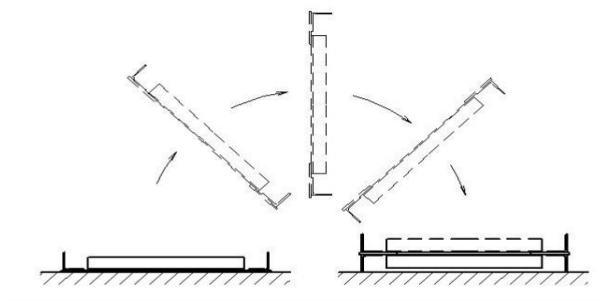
Поворот сварной фермы на 180°
